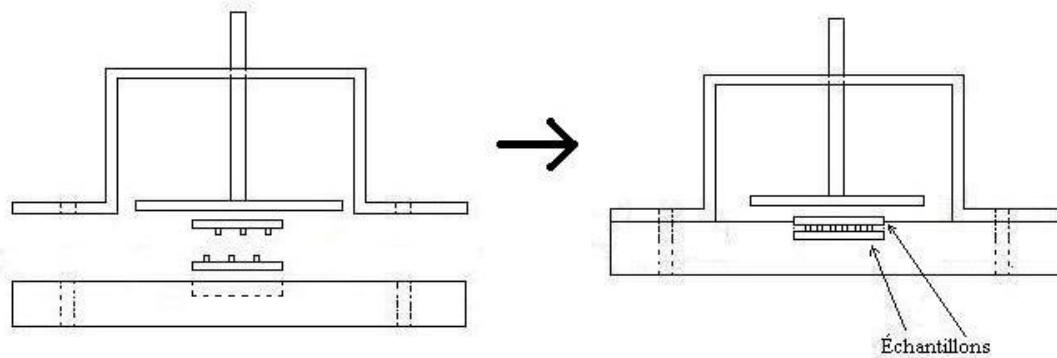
Instrument servant à aligner les deux parties de module pour la seconde soudure. La surface de la cavité est de $6.67\text{mm} \times 6.67\text{mm}$.
